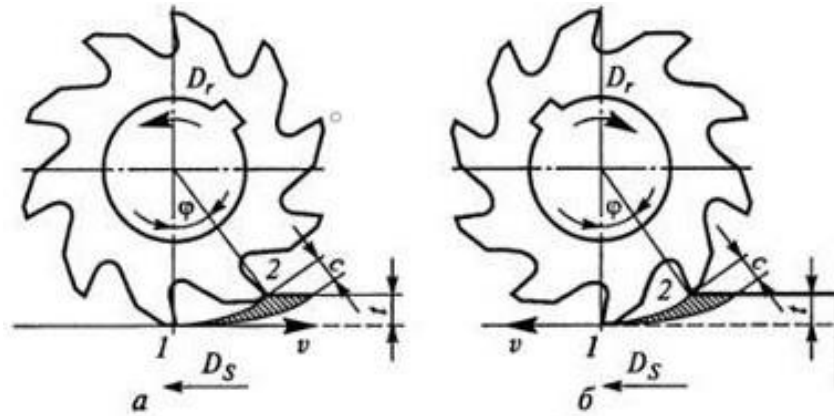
Методы фрезерования: а – встречное; б – попутное
